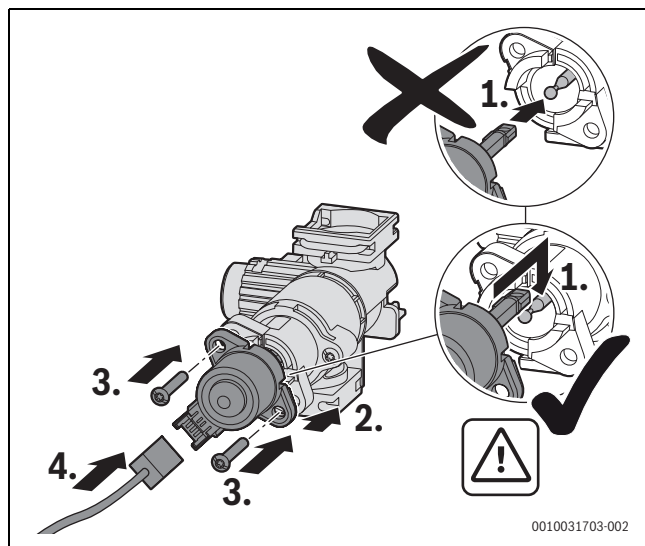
Montare il motore sulla valvola a 3 vie (variante con viti)
